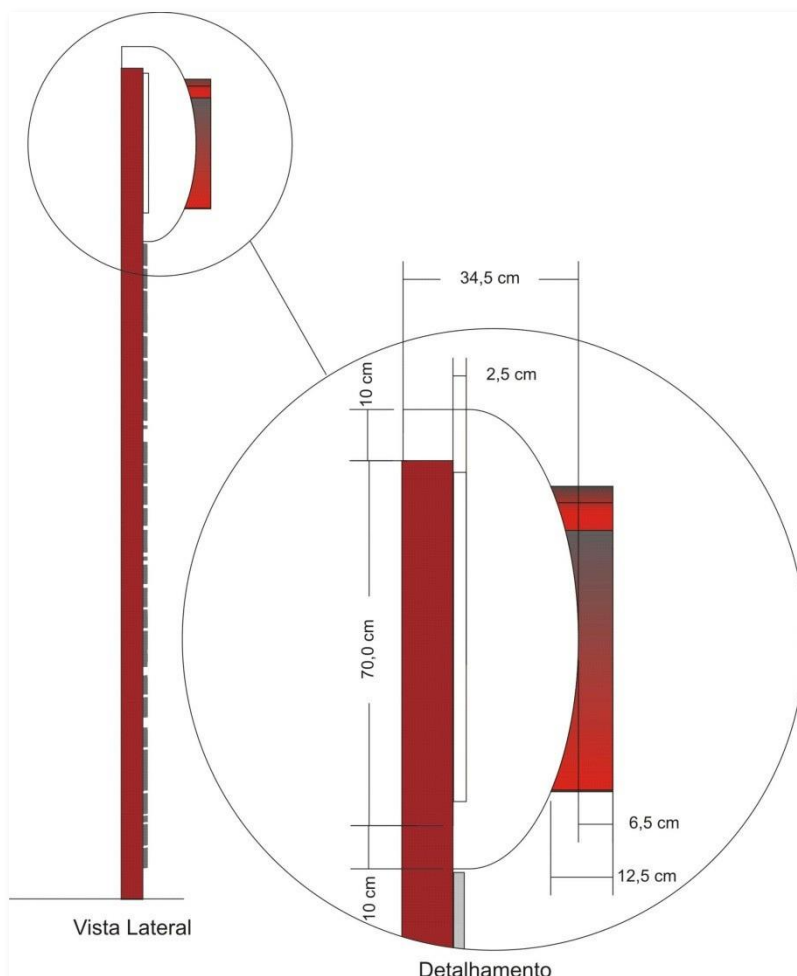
Placa de Fachada - Medidas Laterais e Detalhe
